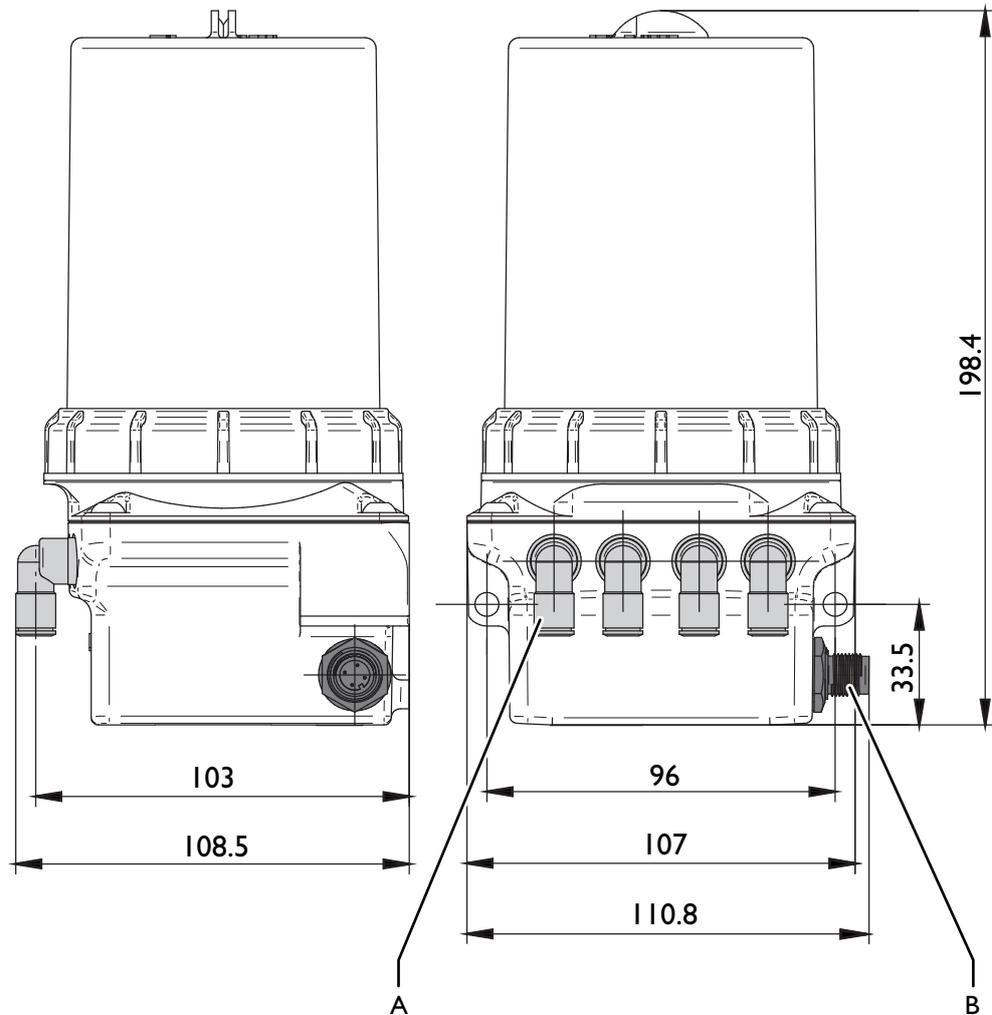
Abmessungen und Anschlüsse FlexxPump4 D
